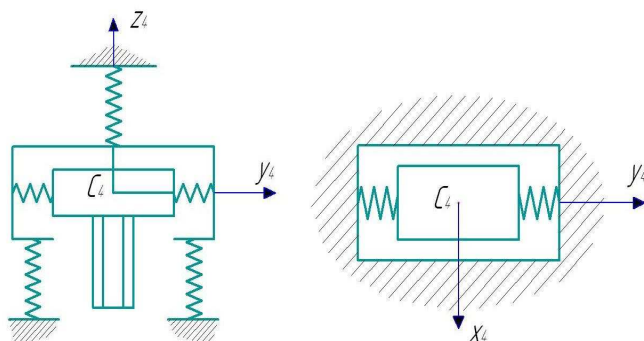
Кинематическая схема упругого закрепления цилиндрической детали в схвате
